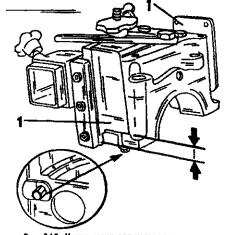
Инструмент для установки крышки заднего подшипника коленчатого вала. Две направляющие пластины (1) прижимают боковые уплотнения в канавки. Уплотнения должны иметь указанные выступы.
